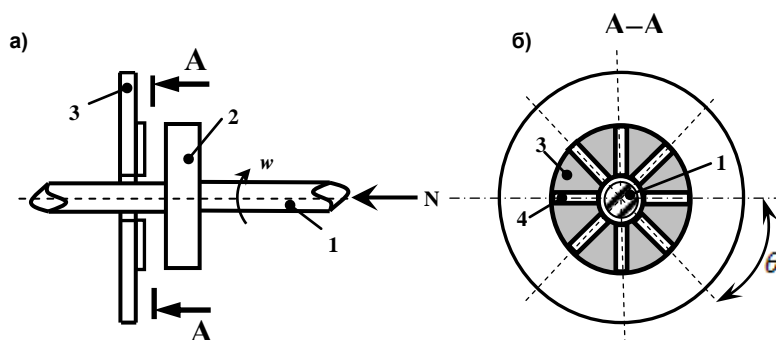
Схема упорного гидродинамического подшипника (а – вид сбоку; б – сечение АА): 1 – ротор; 2 – пята; 3 – подпятник; 4 – канавка
